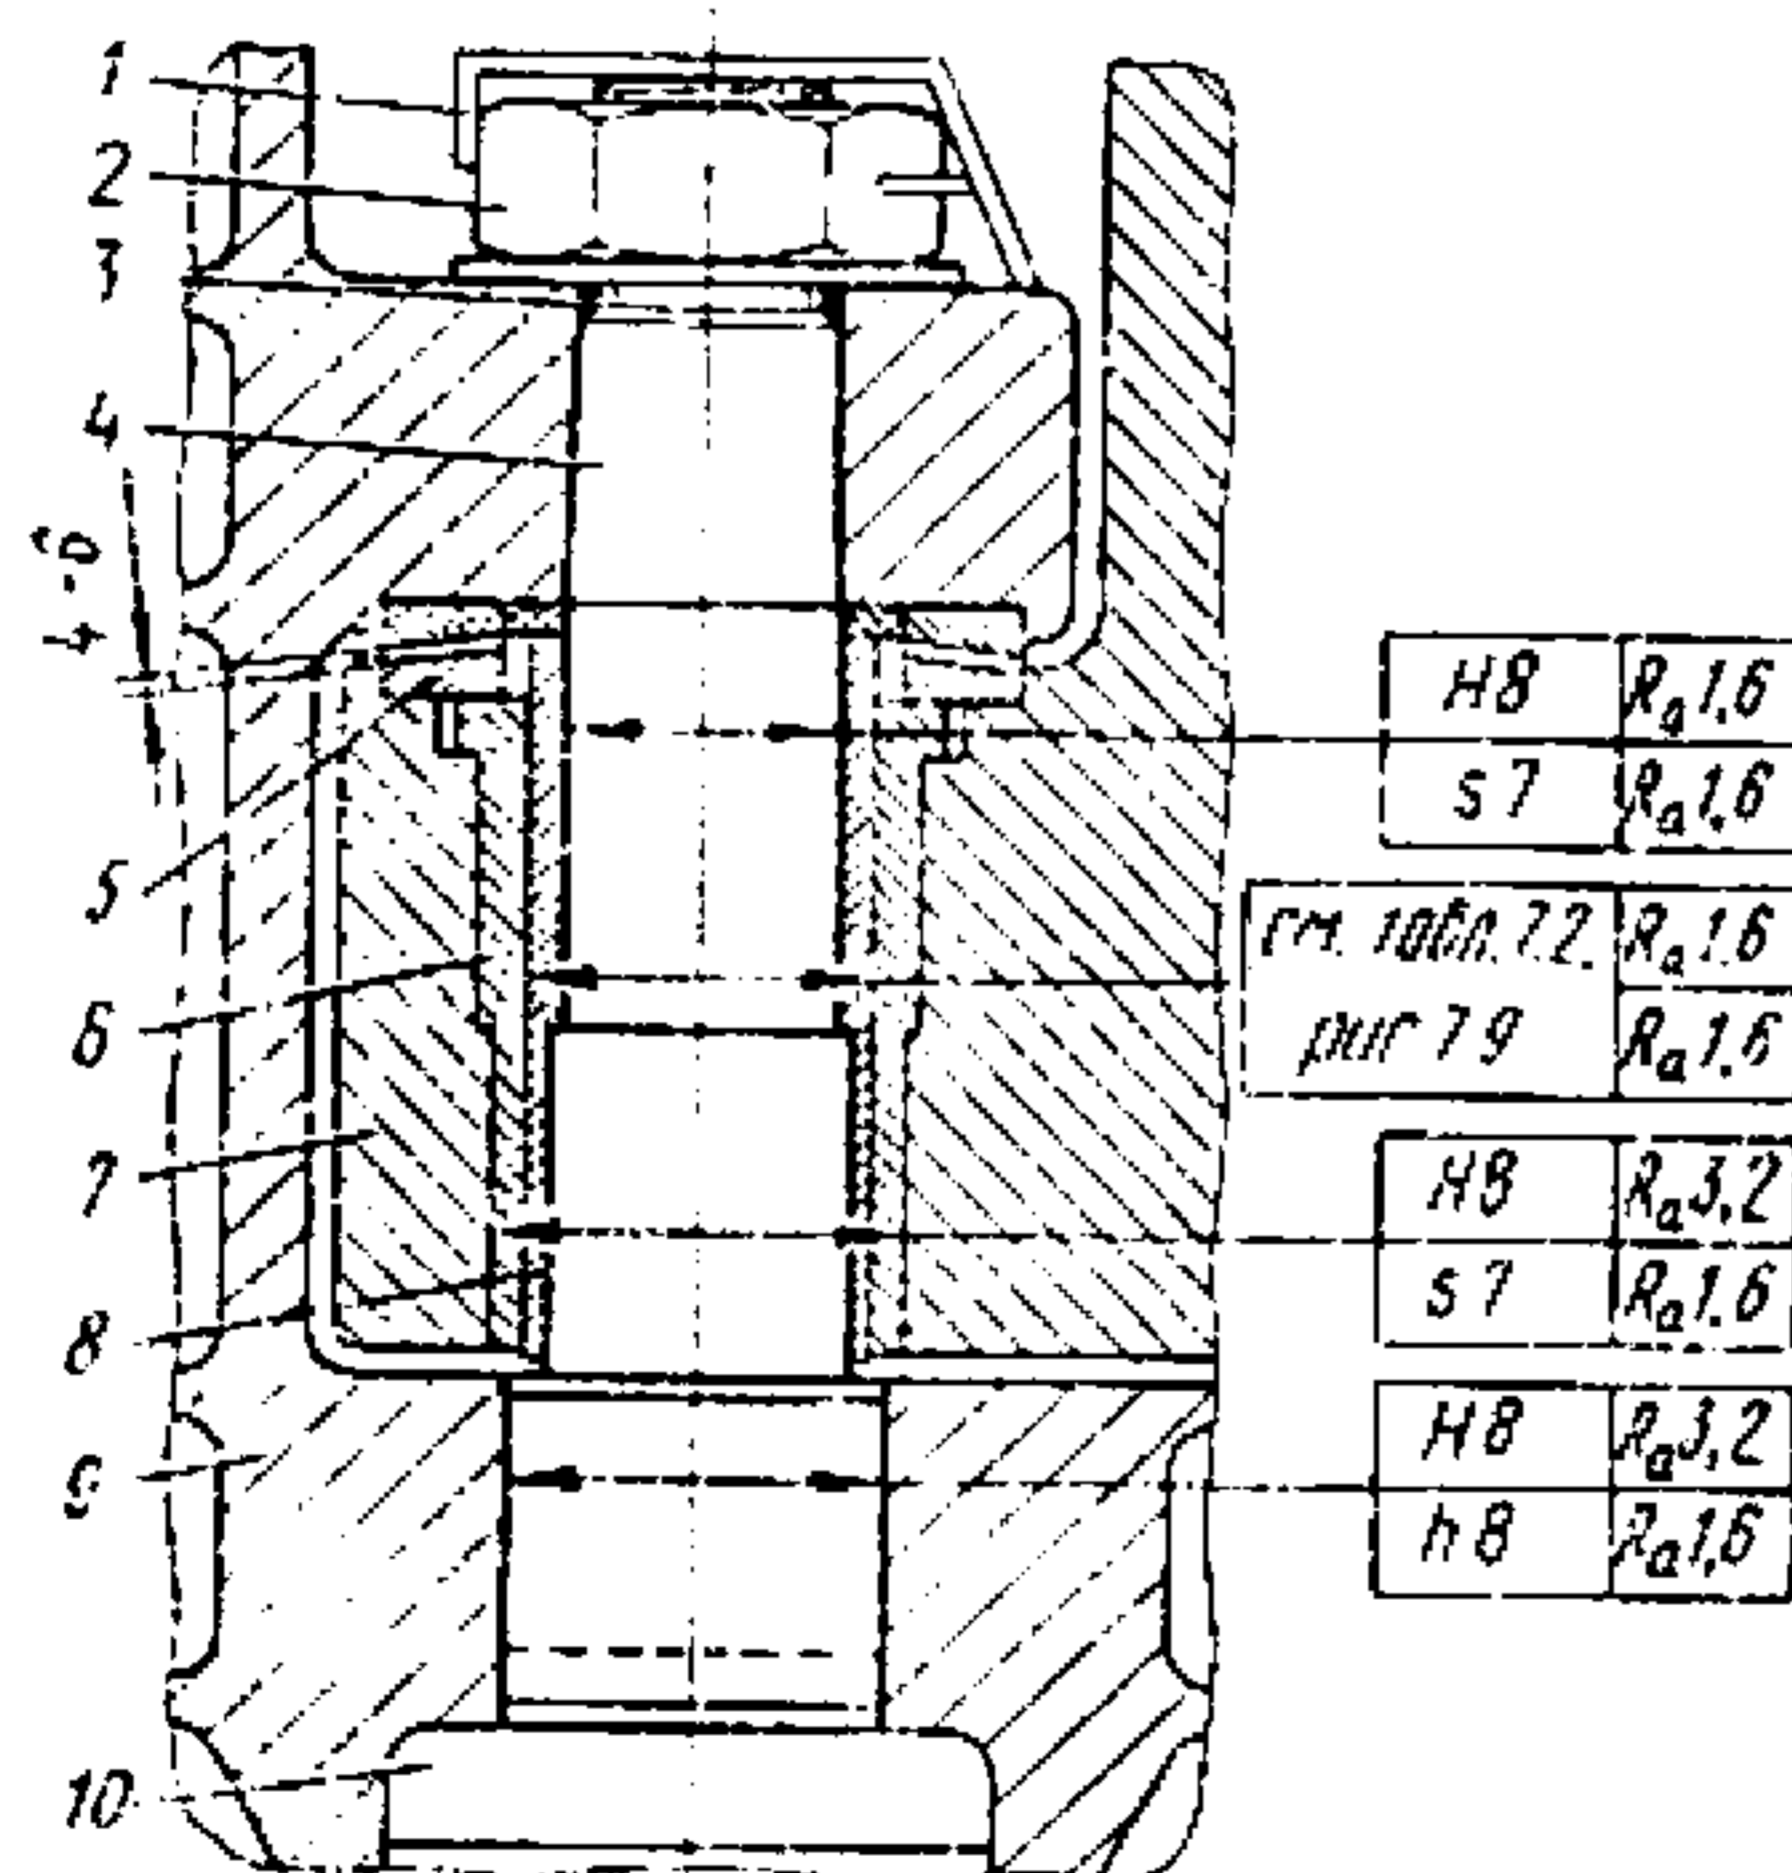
Штырь с цилиндрической направляющей втулкой:
